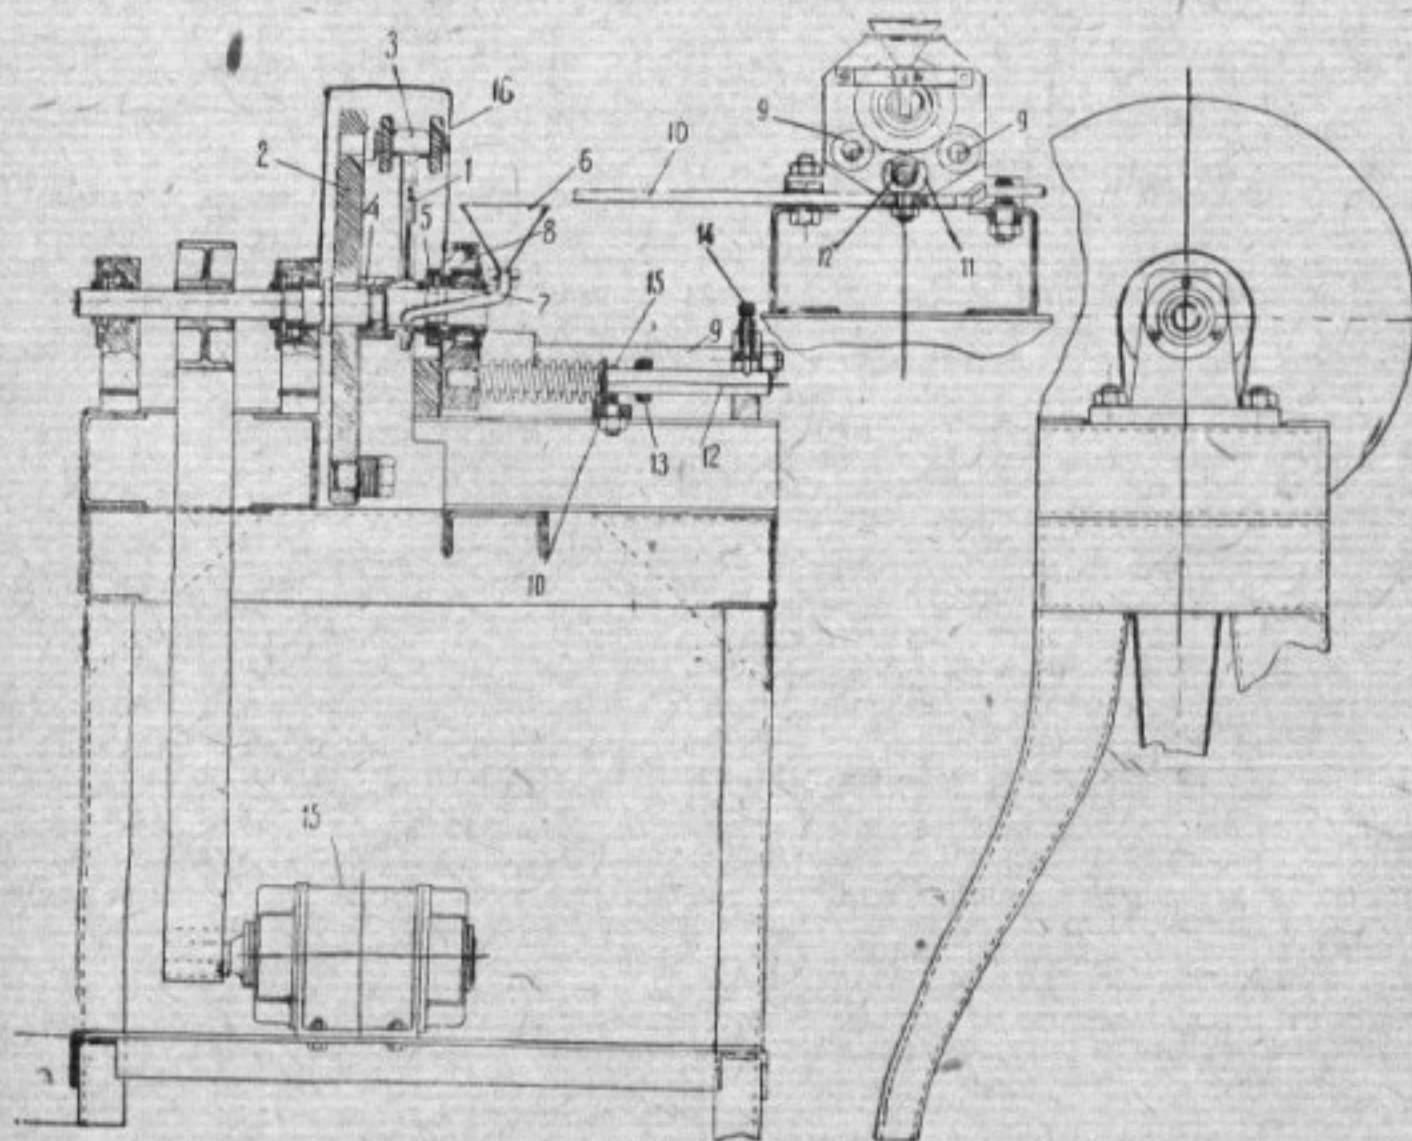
Станок для центробежной заливки шатунов двигателя ГАЗ-А и АА
